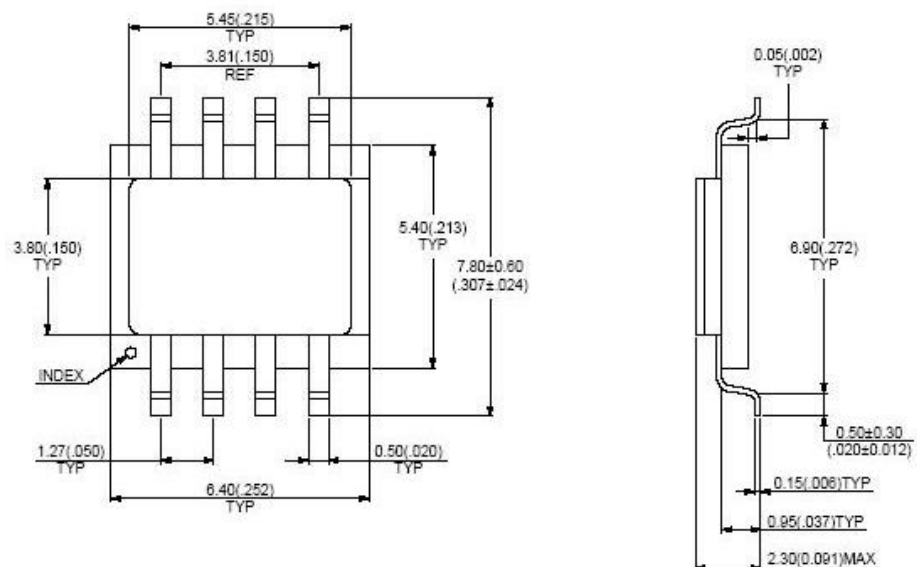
Габаритні розміри корпусу мікросхеми SOP-8
